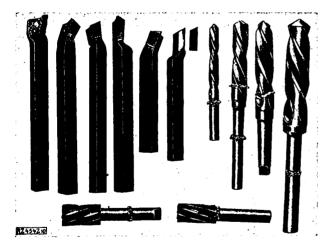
Nach dem Abschmelz-Schweißverfahren hergestellte Werkzeuge
